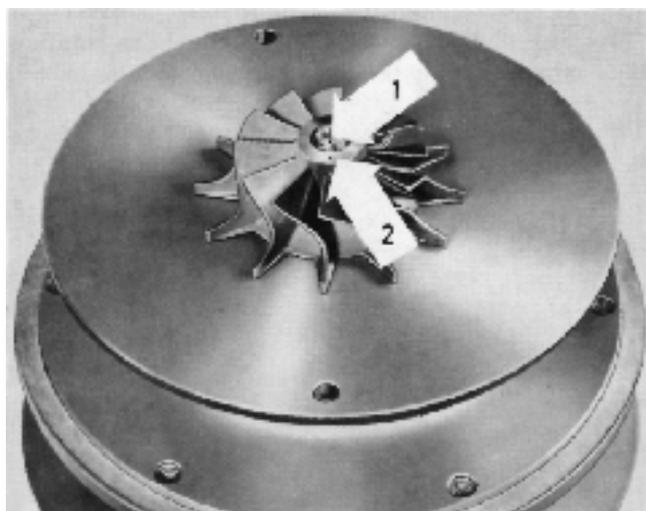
Montage de la roue de compresseur 1 et 2 = repères
